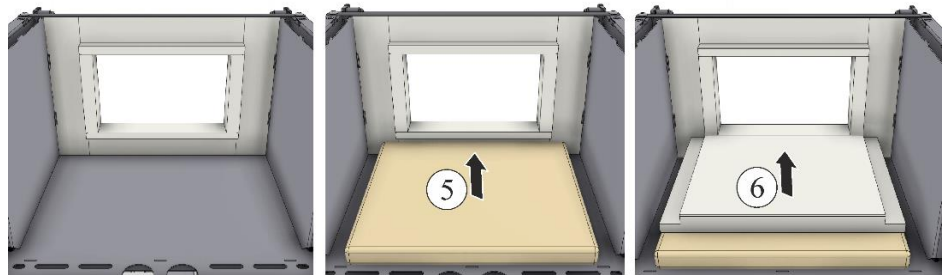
Montaje del panel aislante y la placa de aislamiento inferiores (figura análoga)
